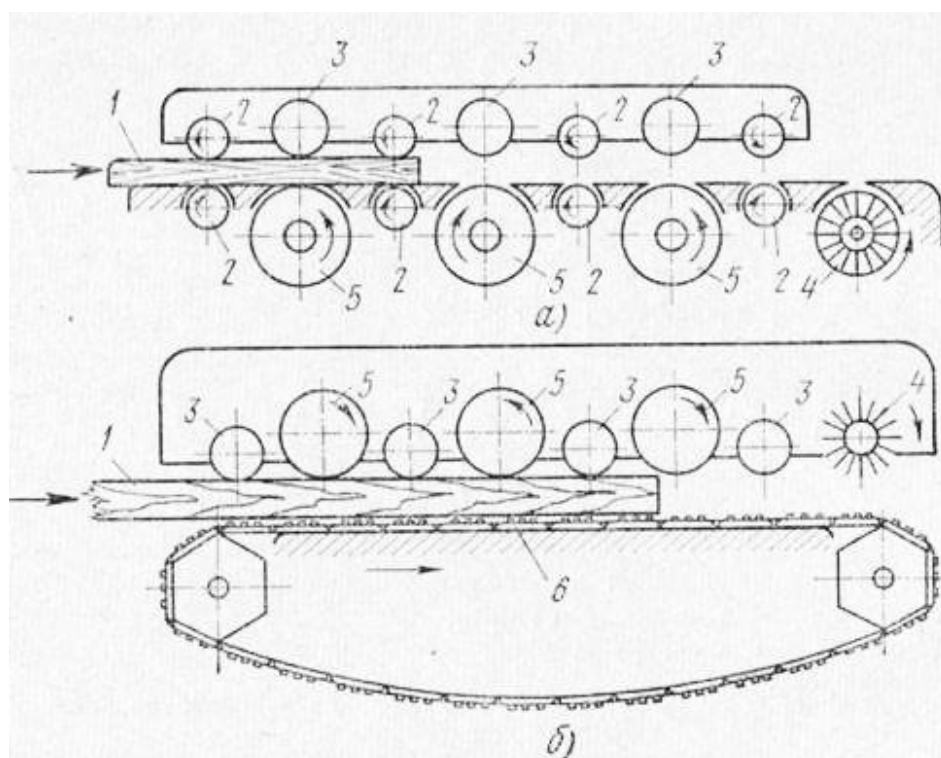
Схемы шлифования заготовок на трехцилиндровых шлифовальных станках: а — с вальцовой подачей, б — с гусеничной подачей; 1 — заготовка, 2 — подающие валики, 3 — прижимные валики, 4 — щеточный барабан для очистки деталей от пыли, 5 — шлифовальные цилиндры, 6 — гусеничная цепь
